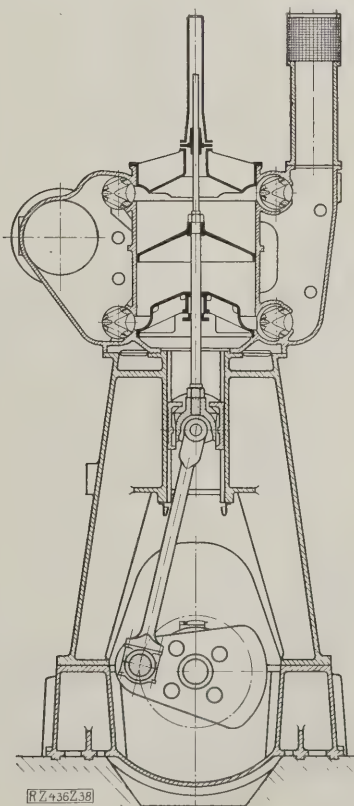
Spül- und Ladepumpe für die Dieselmachine, Abb. 37, mit Corlisssteuerung.
